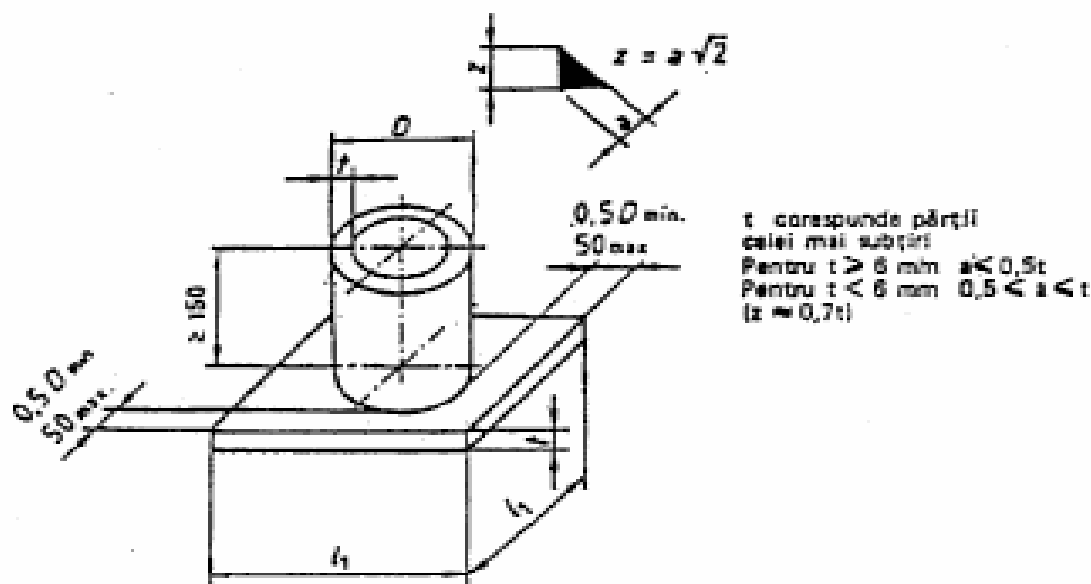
Dimensiunile probei pentru sudura în colț la țevă
